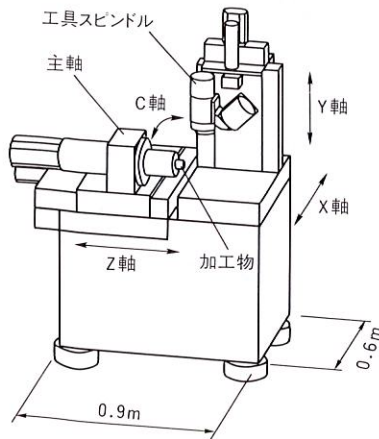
超精密 CNC 加工装置 超精密 4 軸 CNC 加工装置により原盤を切削加工した。
